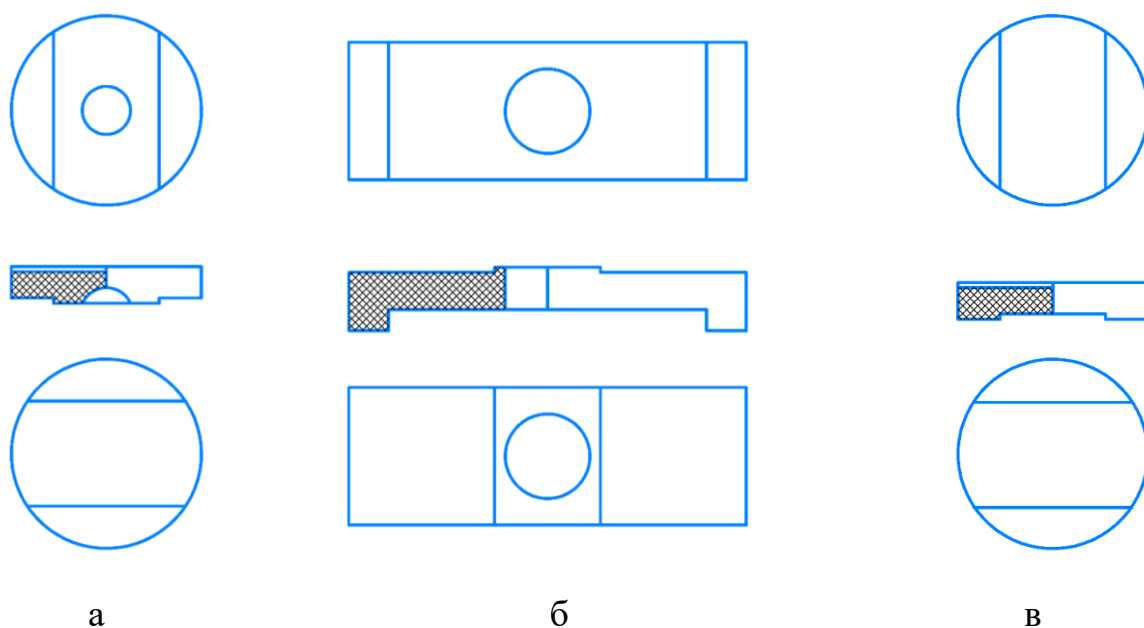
Вид композиционных проставок: а) центровочная шайба; б) проставка с креплением под динамометр; в) проставка с пазом под образец
